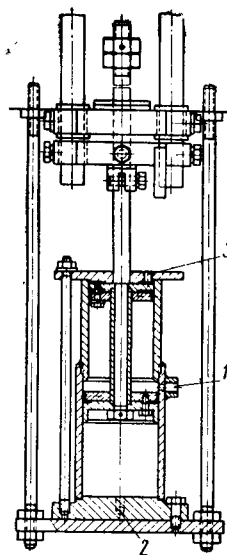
Пневматический цилиндр выталкивающего устройства.
